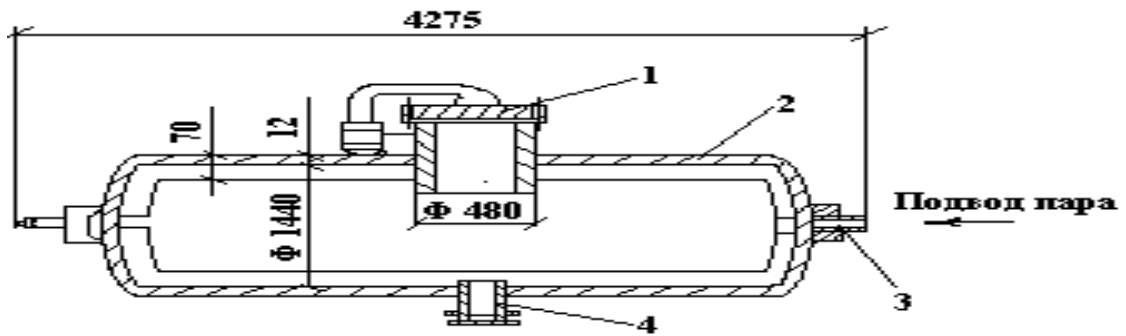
Общий вид вращающегося автоклава: 1 – загрузочный люк; 2 – корпус; 3 – полая цапфа; 4 – сливной патрубок
